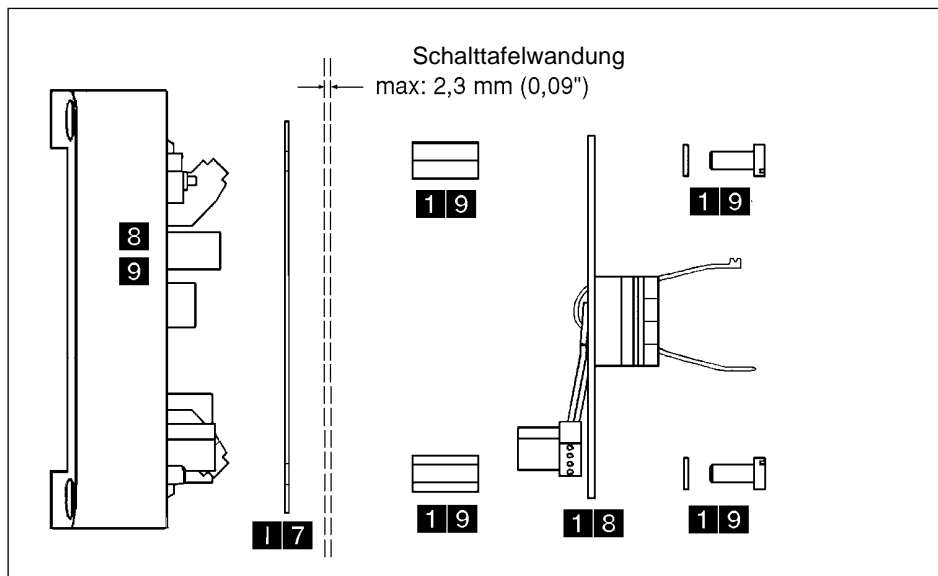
Ersatzteil-Explosionszeichnung 8025 Schalttafel-Ausführung
